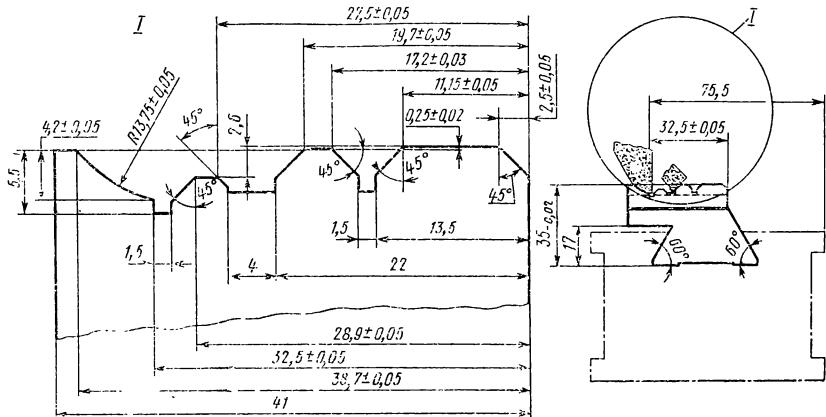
Профиль и схема шлифования резца для обработки шести фасок под углом 45° и дуги
